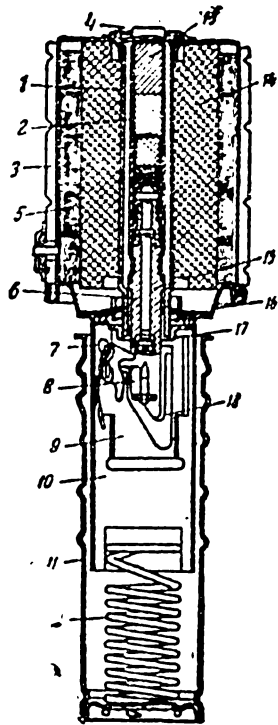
Разрез гранаты: 1—центральная трубка; 2—запал; 3—защитный чехол; 4—выдвижка запала; 5—металлическая лента; 6—дистанционная трубка; 7—защитный чехол; 8—боевая скоба с ударником; 9—примёр; 10—внутренняя трубка рукоятки; 11—рукоятка; 12—боевая пружина; 13—дополнительный детонатор; 14—разрывной заряд; 15—дистанционная часть запала; 16—дно корпуса; 17—капсюль-воспламенитель; 18—прорези.
